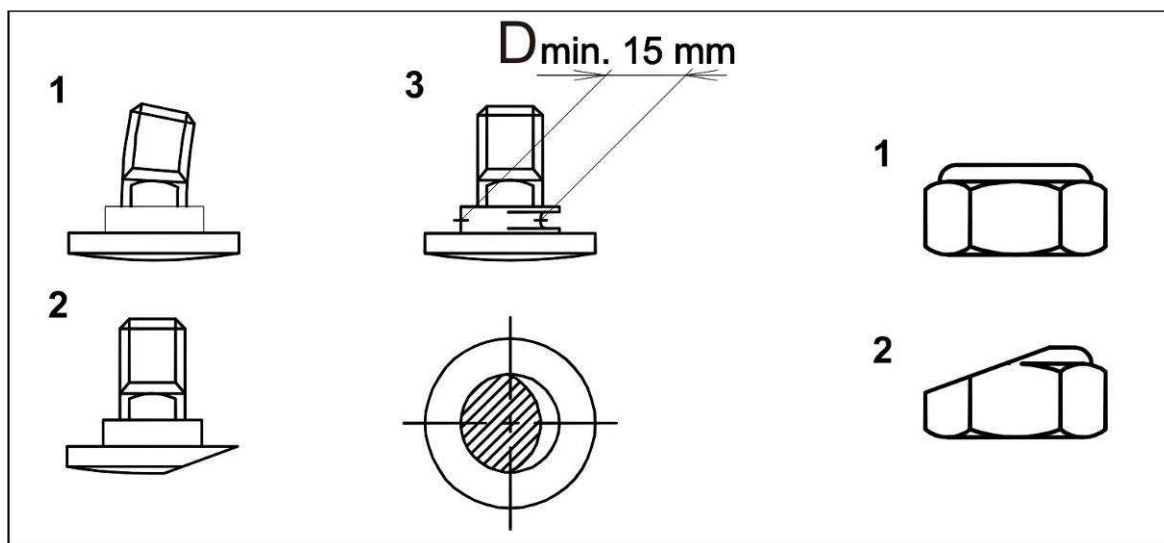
Замена болтов и гаек крепления ножей
